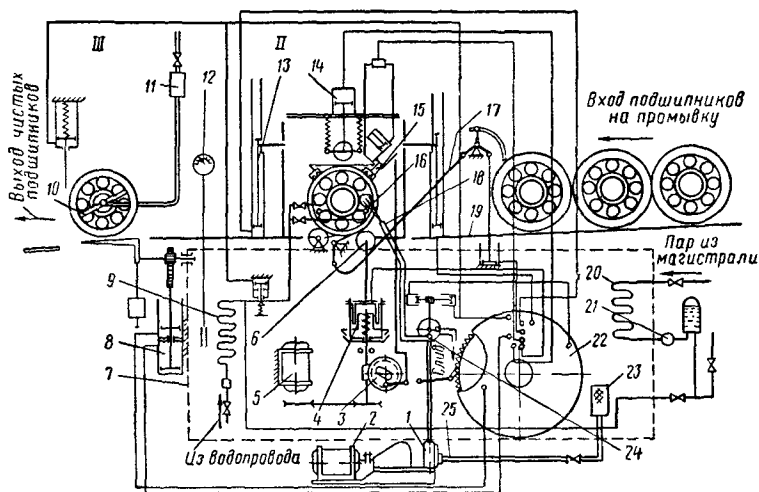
Принципиальная схема полуавтоматической установки для очистки роликовых подшипников:
